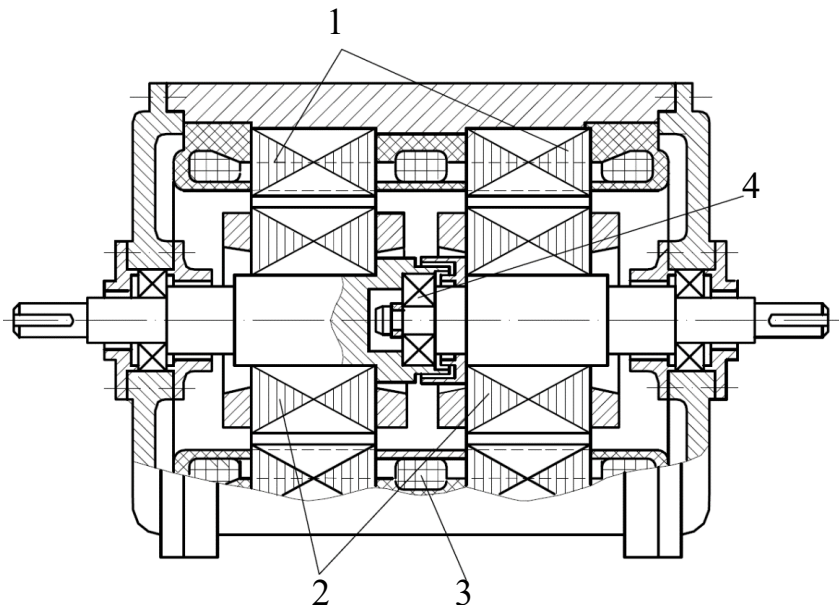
Конструктивна схема секційованого асинхронного двигуна зустрічного обертання: 1 – секційований статор; 2-ротор; 3 – міжсекційна ділянка обмотки статора; 4 – підшипник подвійного обертання.
